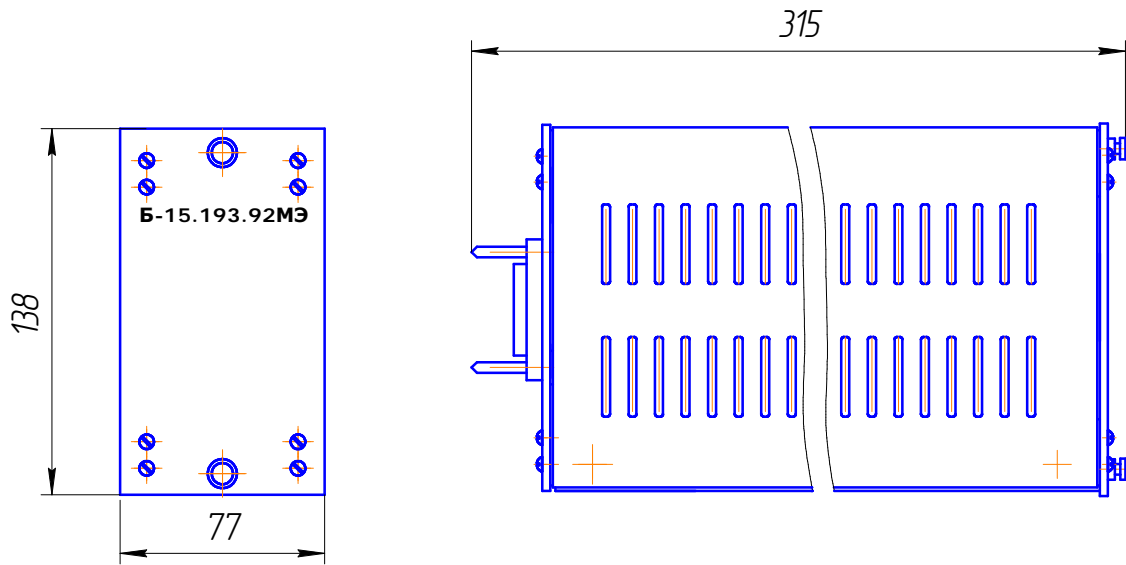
Габаритный чертеж каркаса смонтированного
